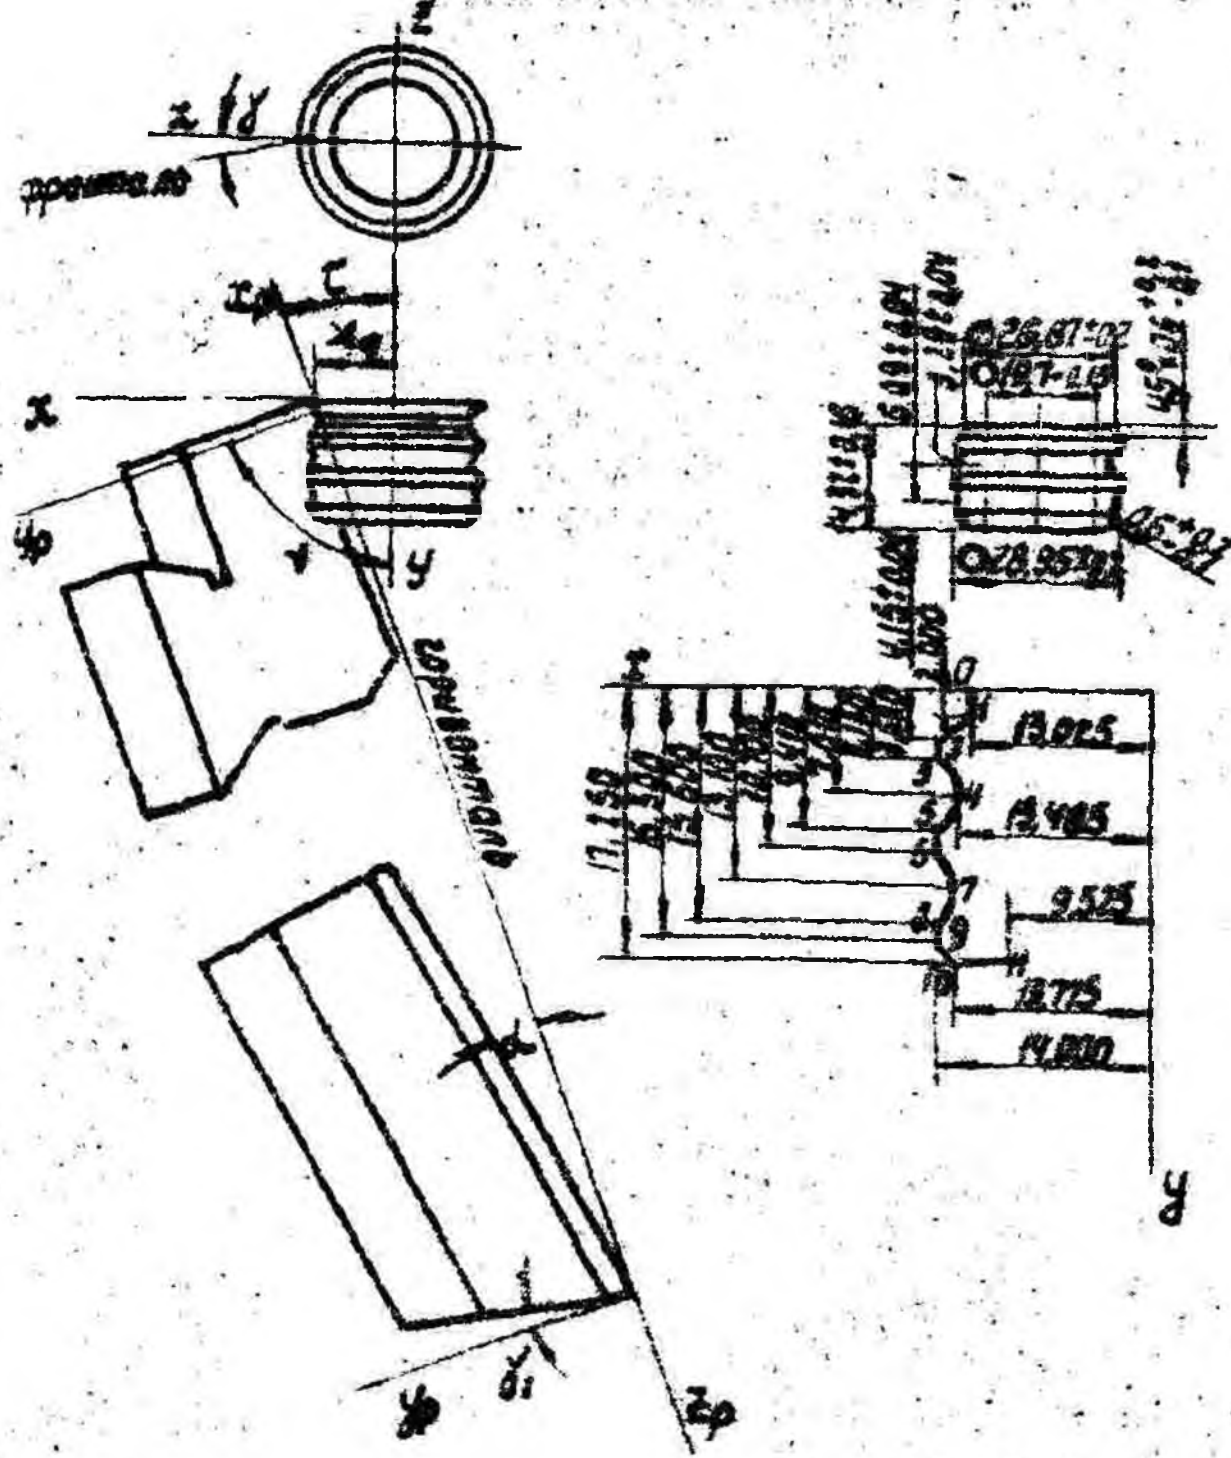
Профиль и размеры внутреннего кольца подшипника I204; установка резца
